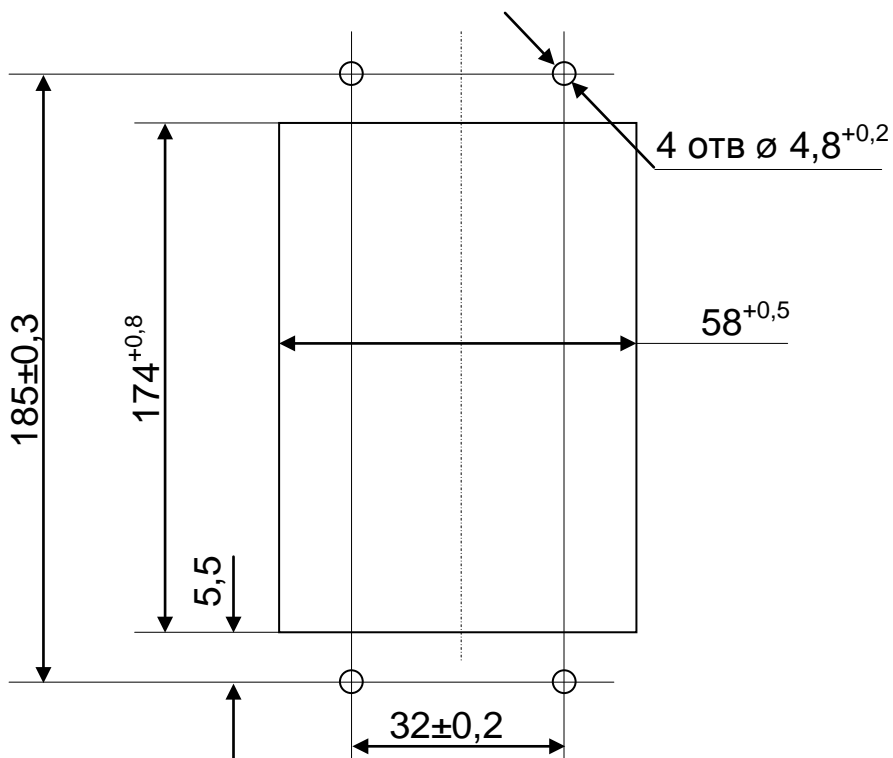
Разметка щита для крепления УЗА-АТ на узкой стороне
